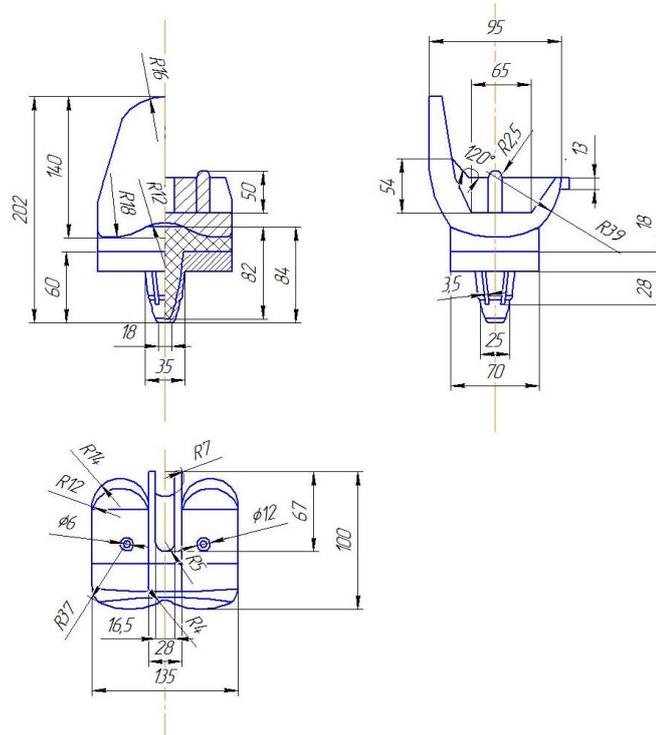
Чертеж конструкции эндопротеза коленного сустава
